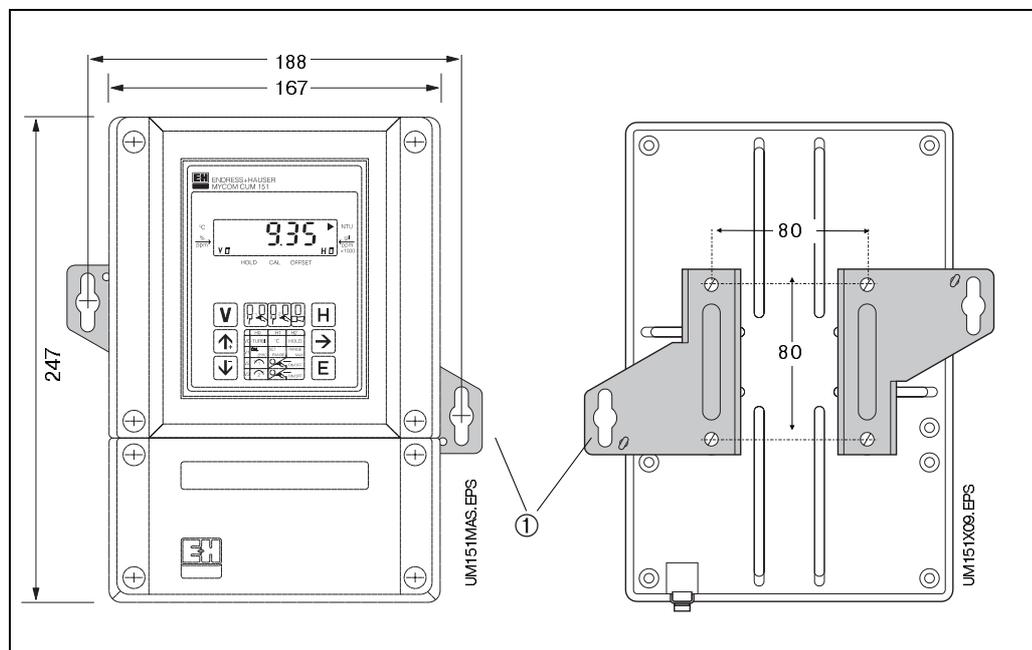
Габаритные размеры (слева) Mycom CUM 151
